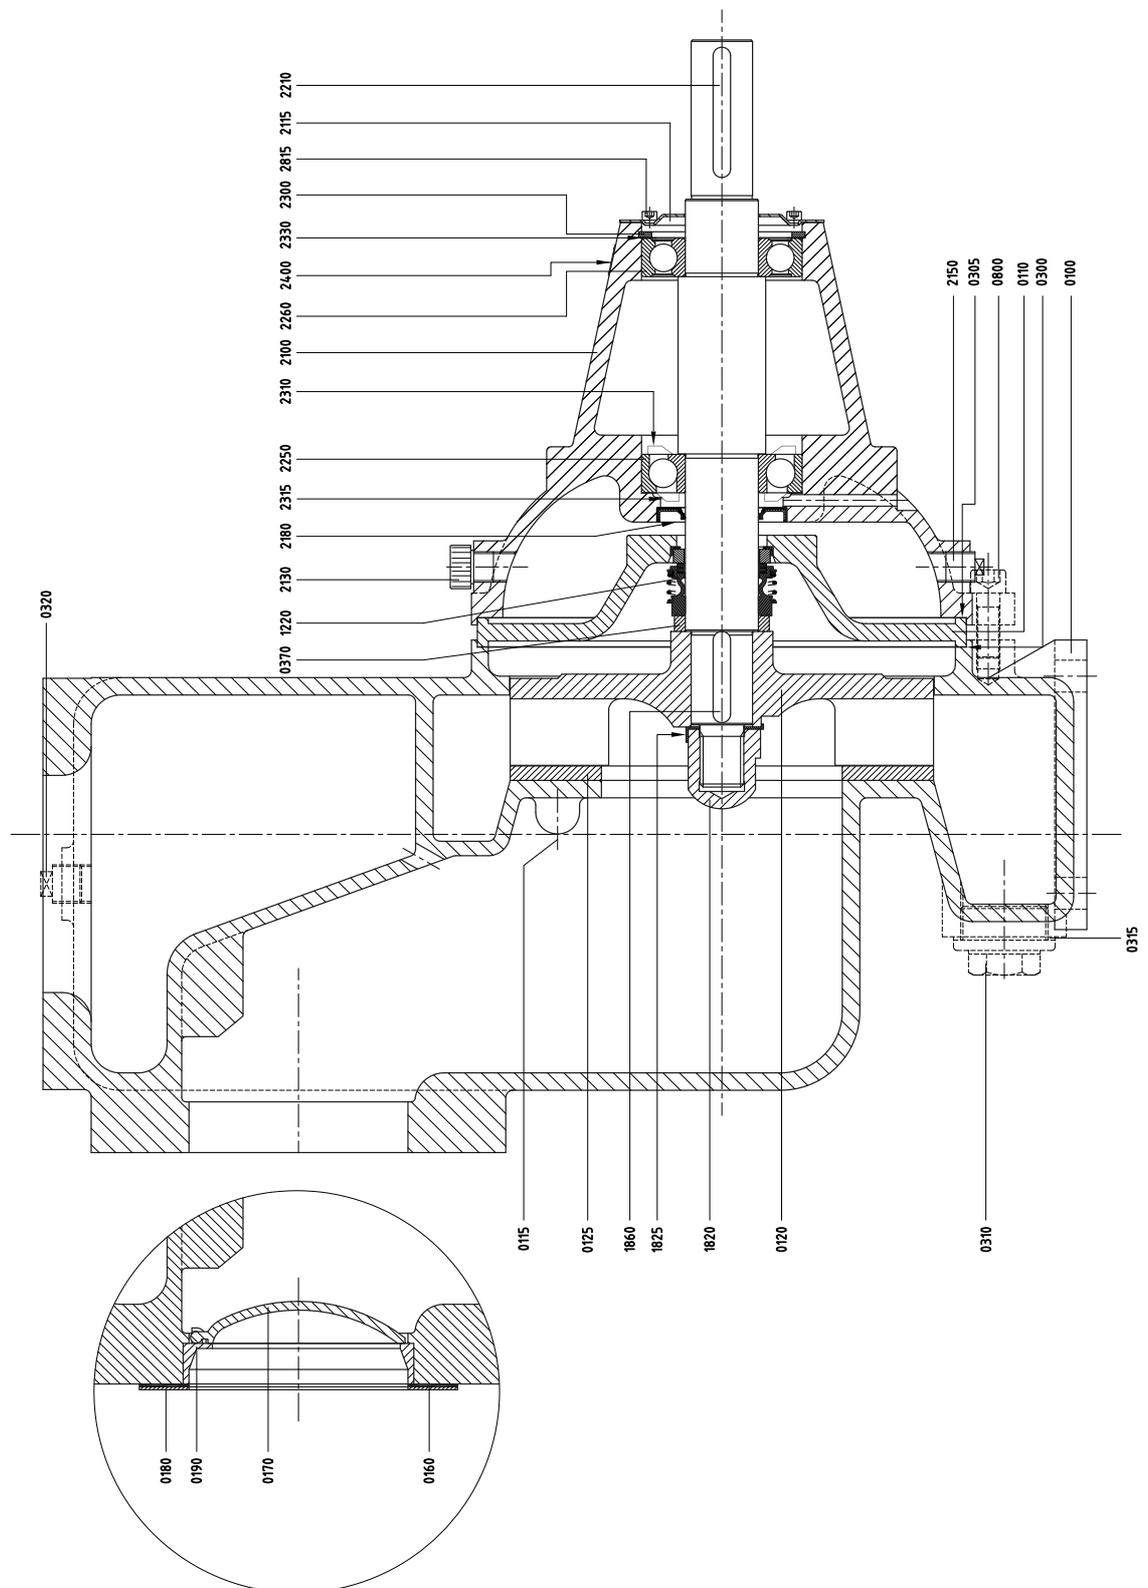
Schnittzeichnung FRE 150-290b und 150-290.
